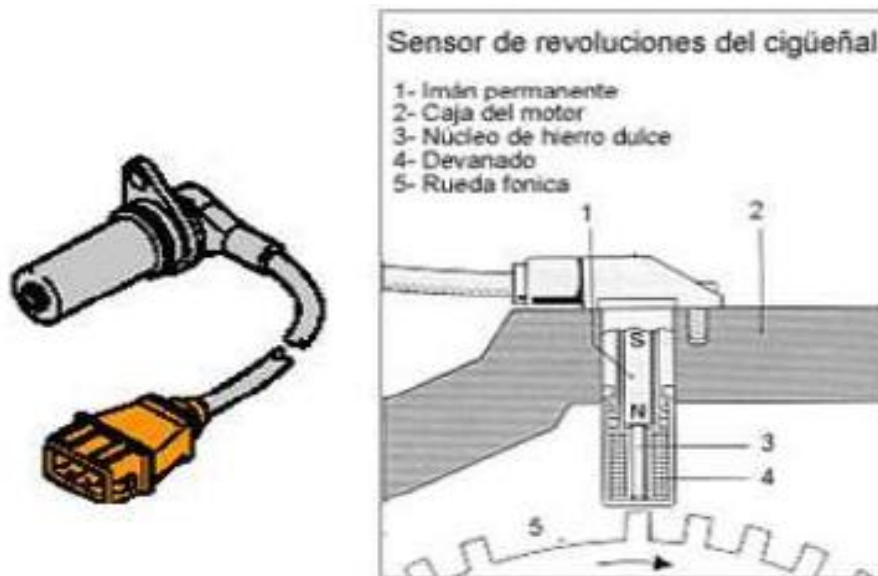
Constitución del Sensor de Posición del Cigüeñal.
